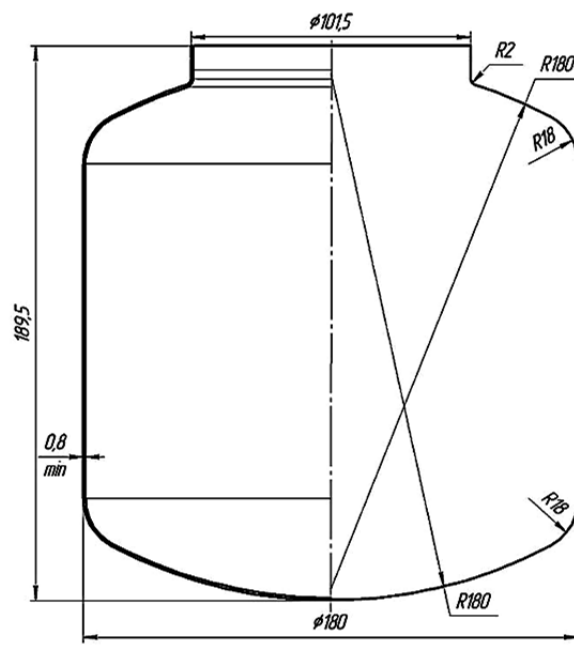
Заготовка після процесу ротаційного обкочування з горловиною
